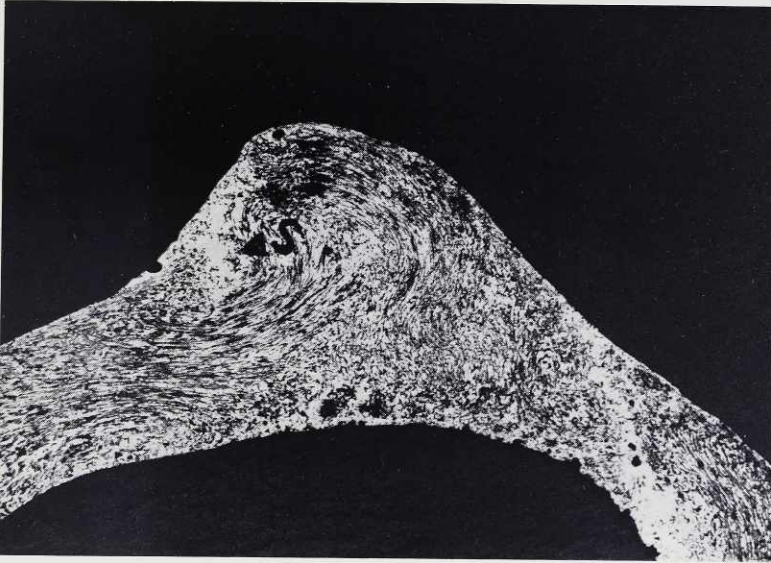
Querschliff der Schweißstelle auf einem Kettenglied, geätzt. Maßstab 35:1.
